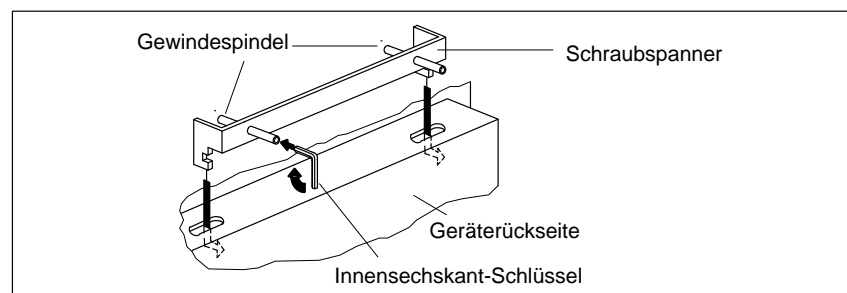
Einhängen und Festdrehen der Schraubspanner
